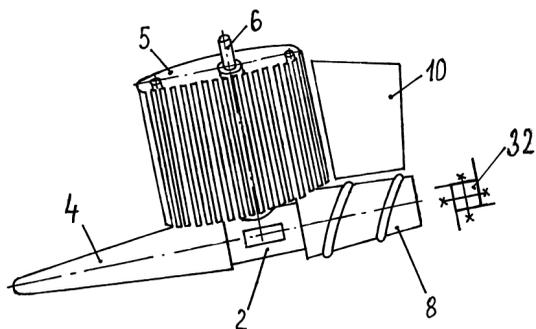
Корнеизвлекающее устройство (вид сверху)
